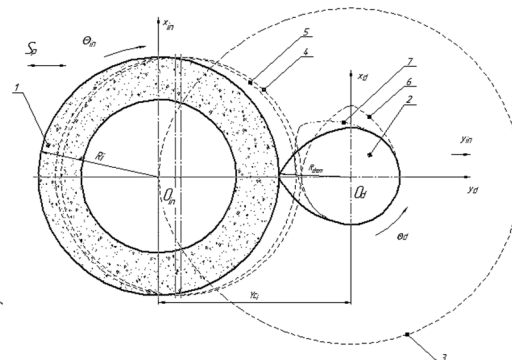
Схема обробки кулачка розподільного вала фірмою Junker
